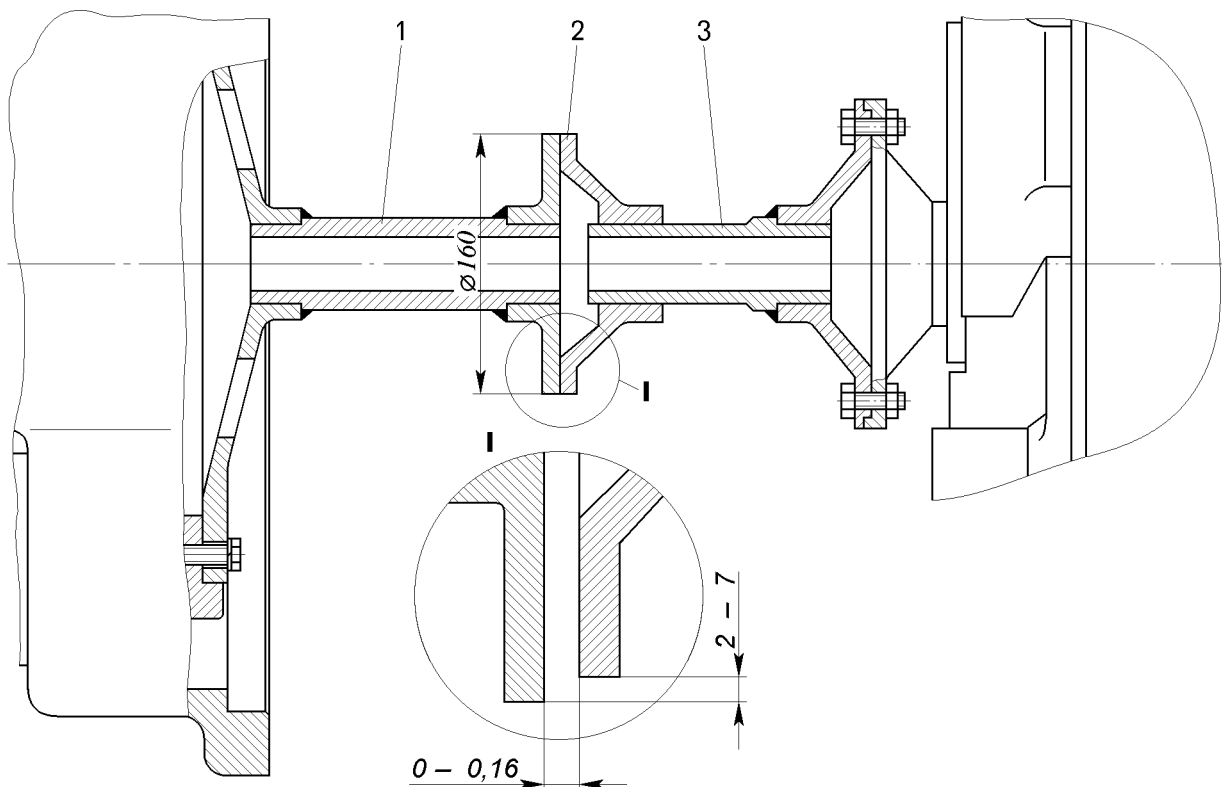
Приспособление для проверки соосности и параллельности осей ведущего вала гидромеханической передачи и коленчатого вала двигателя:
